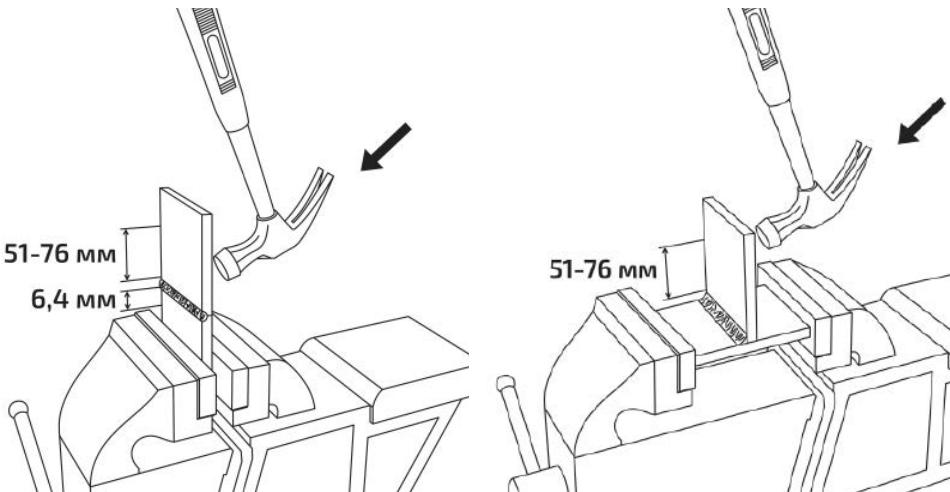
Проверка на прочность сварного соединения.
